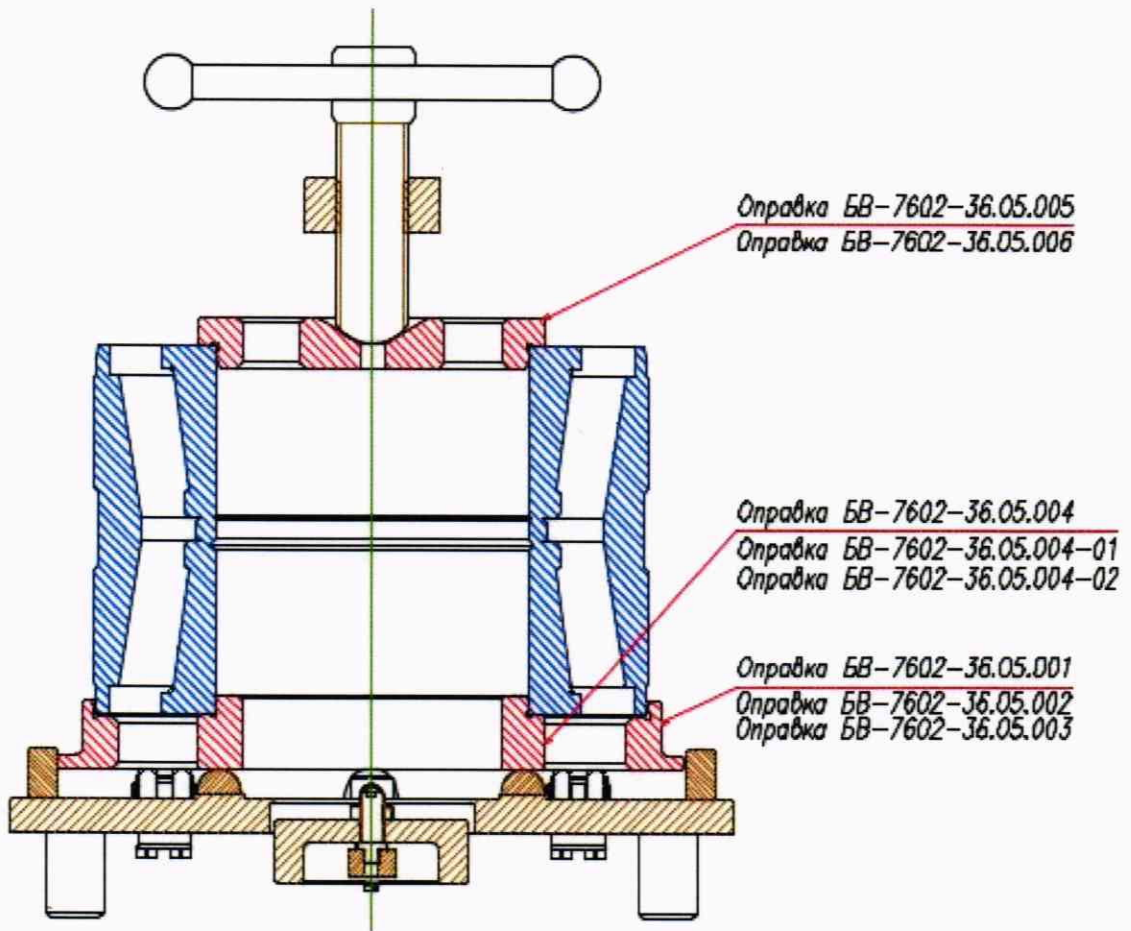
Схема установки подшипника на Приборе БВ-7602-36
